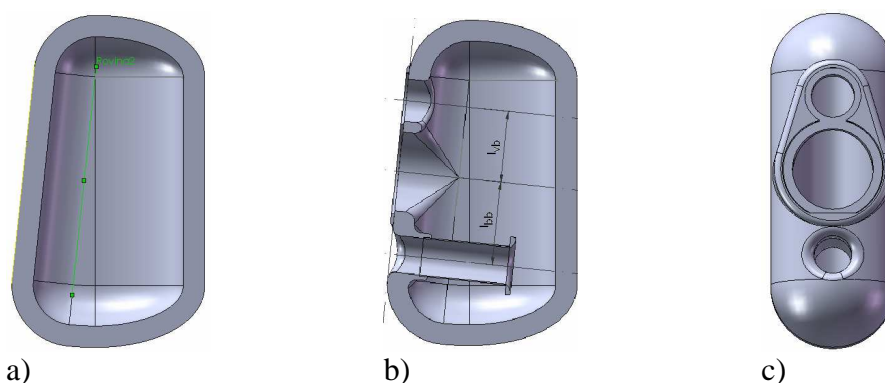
a) Boční pohled tělesa dutiny ozvučnice
